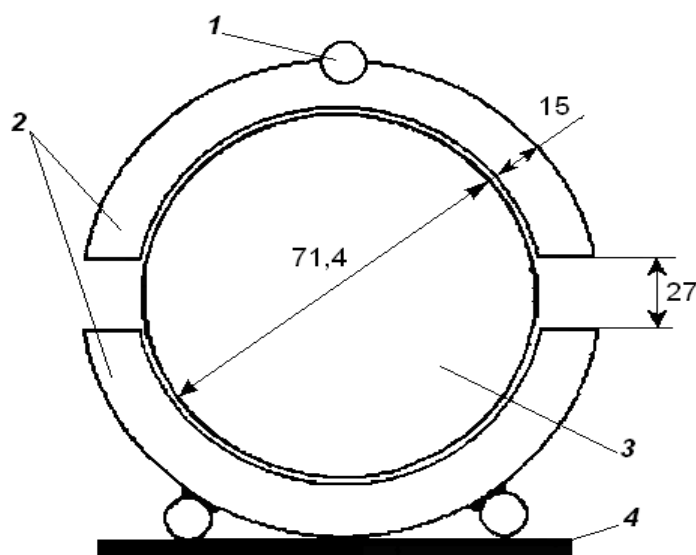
Обжимное устройство: 1 – шарнир; 2 – цилиндрические обоймы; 3 – образец; 4 – нижняя плита пресса
